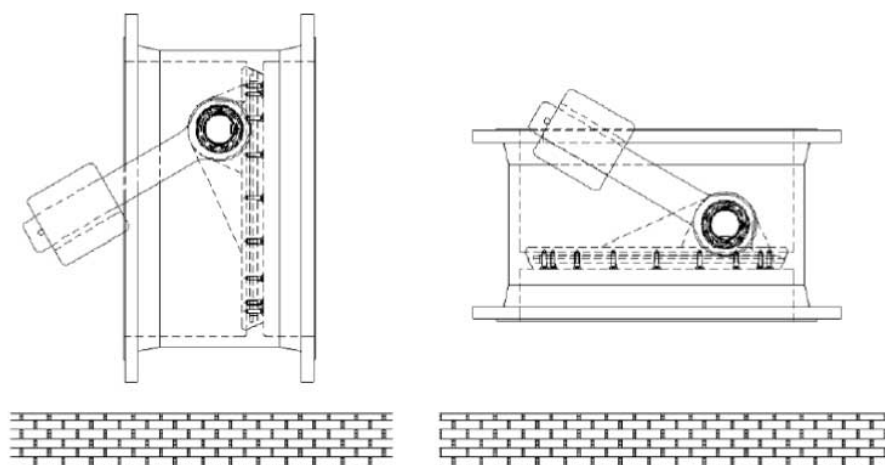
vertikale und horizontale Einbaulage COBRA-TDC01/03
